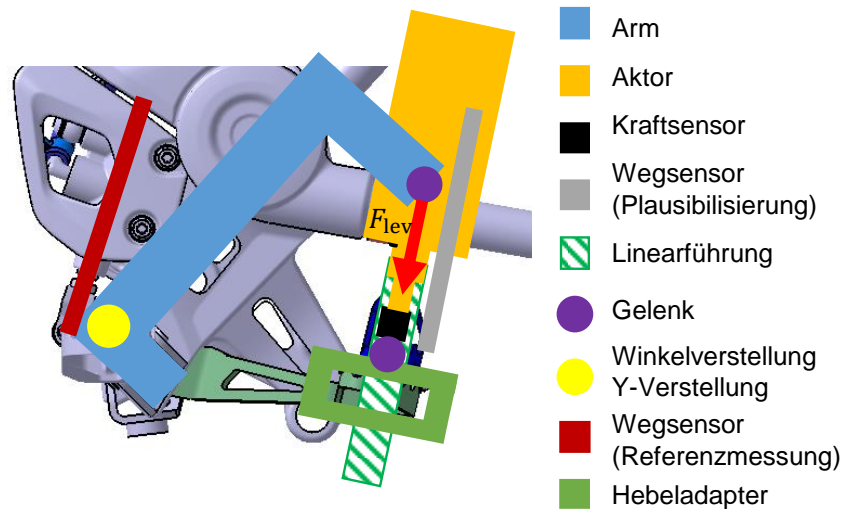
Prinzplösung H1 für die hintere Messeinrichtung. Drehbar gelagerte Aktorik betätigt den Fußbremshebel linear mittels Druck. Referenzwegmessung am Hauptbremszylinder.
